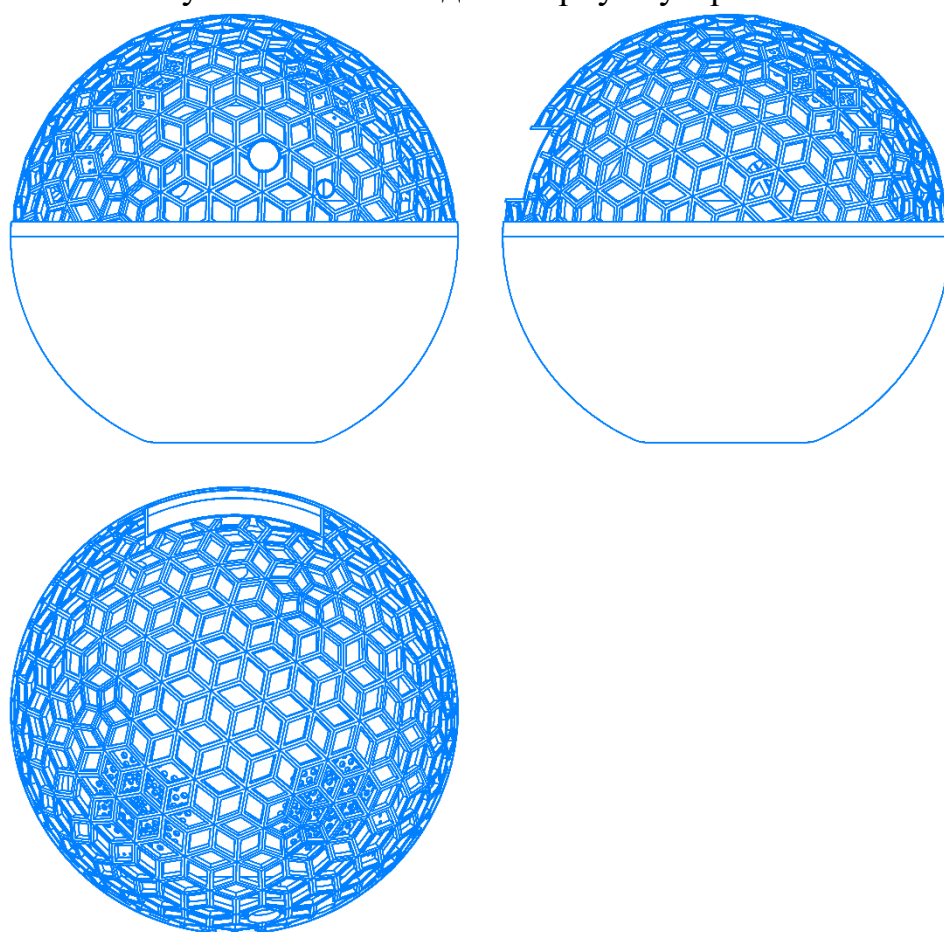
Стандартные проекционные виды модели корпуса устройства (слева сверху – вид спереди, справа сверху – вид сбоку, снизу – вид сверху)
